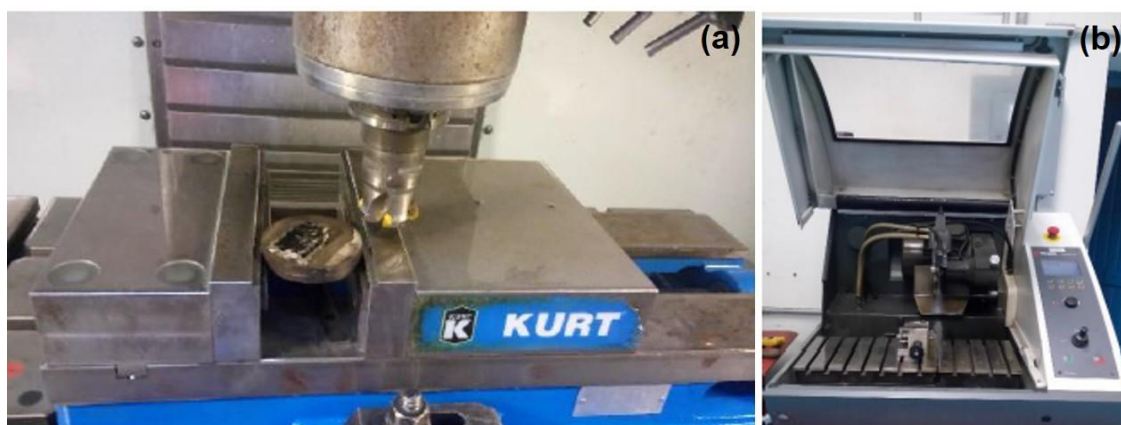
Fotografías de (a) fresadora CNC y (b) cortadora de disco.
